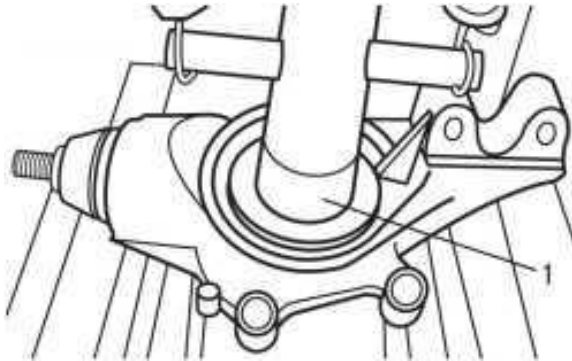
Запресування підшипника в цапфу: 1 – оправка
